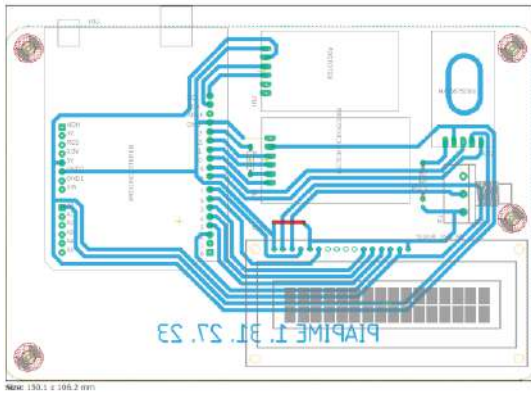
Estructura del diseño de PCB realizado en Eagle de Autodesk.
